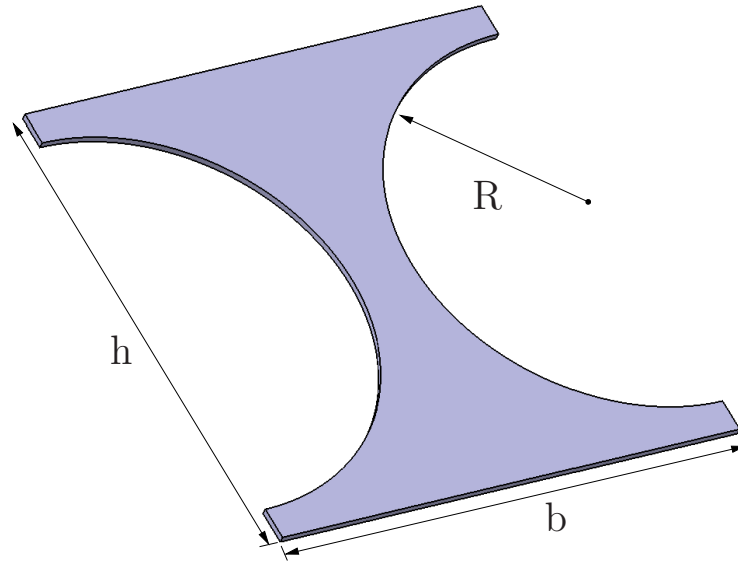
Nakajima-Probe mit $R = 60$ mm aus einer Platte ($h = 150$ mm, $b = 150$ mm, $d = 2$ mm)
